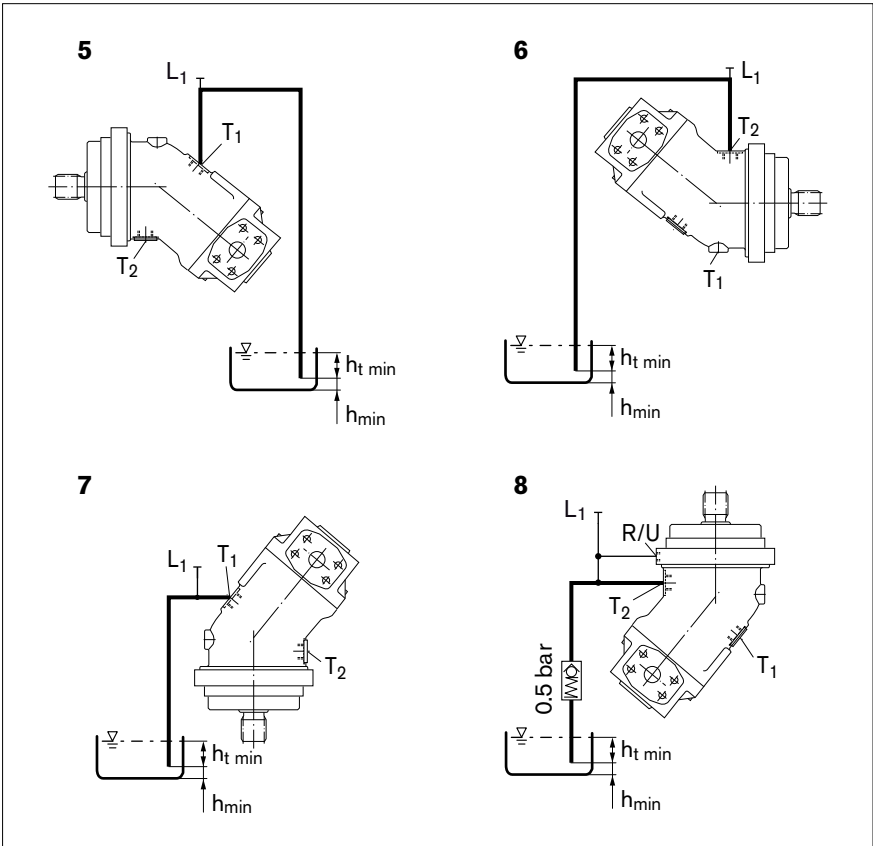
Montaje sobre el tanque con posiciones de montaje 5–8
